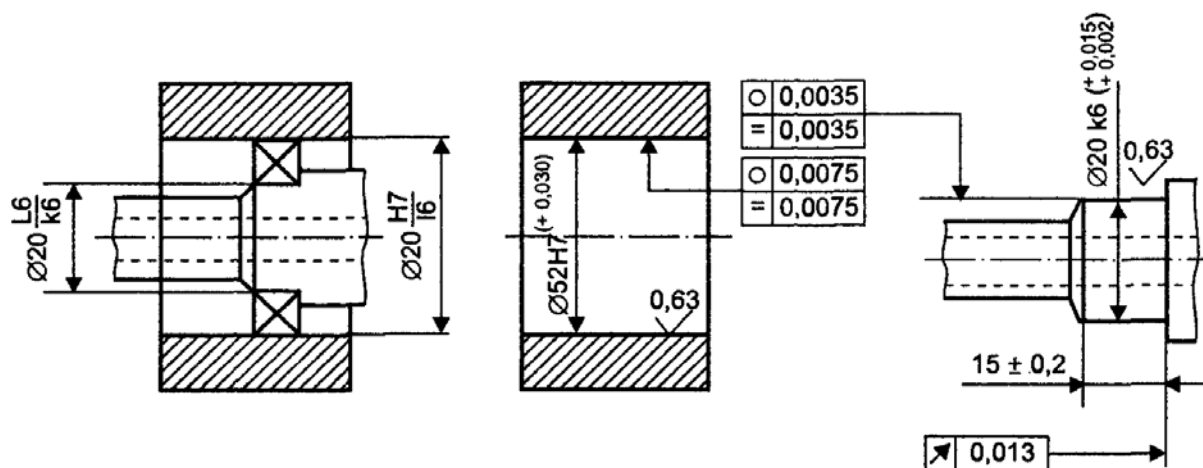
Эскизы подшипникового узла, вала и отверстия
